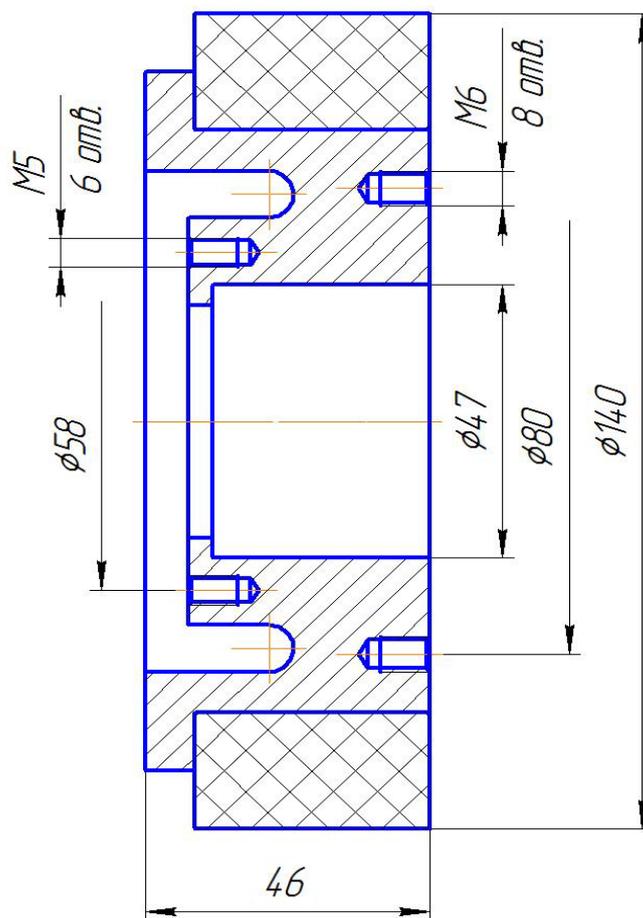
Пример простановки размеров на сборочном чертеже «Колесо»
